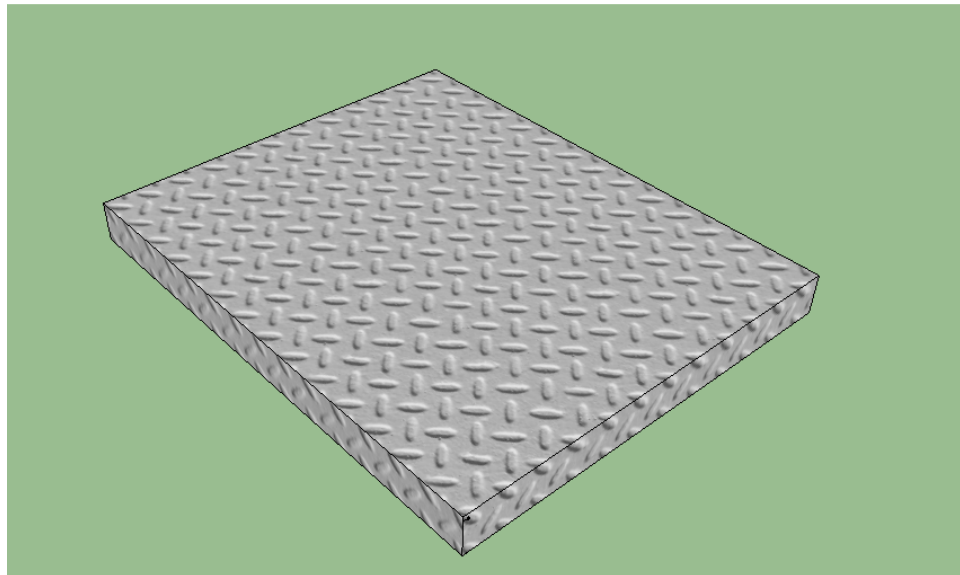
Plancha de asentamiento del neumático, vista isométrica superior.
